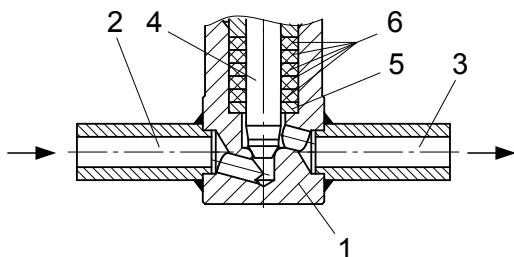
Схема запираания потока рабочей среды в изделиях: 1 - корпус; 2 - входной штуцер; 3 - выходной штуцер; 4 - игла; 5 - шайба; 6 - уплотнительные кольца (набивка)
